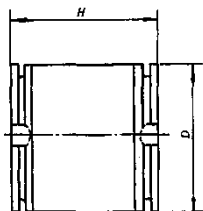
MYL3 型压敏电阻器外形结构尺寸图
